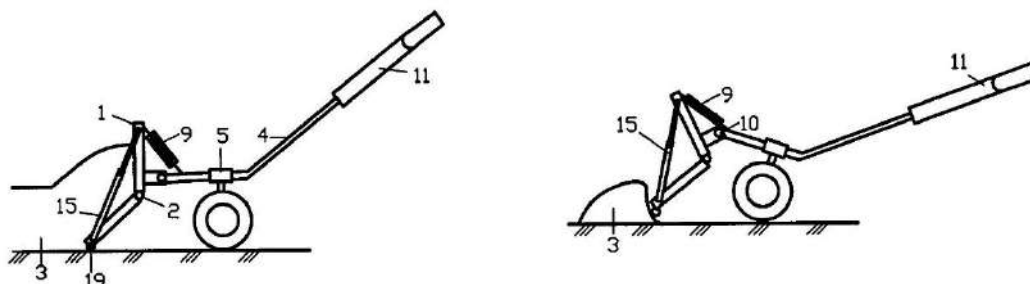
Рычажное снегоуборочное устройство: 1–щит-трансформер; 2 – ось; 3– снег ; 4 – черенок; 5 – патрубок; 6 – ось ОПМ; 7 – колеса; 8 – телескопический кронштейн; 9 – возвратная пружина; 10 – шарнирное соединение; 11 – рукоятка; 12 – винт; 13 – отверстие; 14 – упорный винт; 15 – растяжки; 16 – муфта сцепления; 17 – тросик; 18 – защелка; 19 – ролики.
